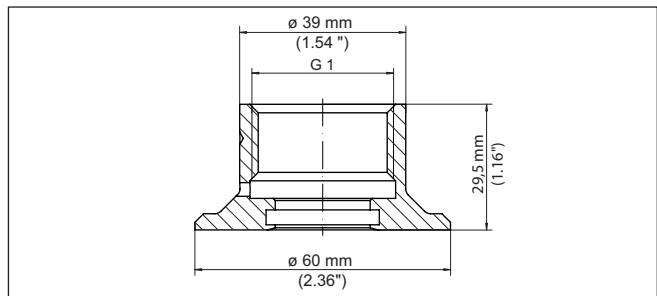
Maße Einschweißstutzen G1 (DIN 3852-A, ISO 228-1) mit Leckage-Bohrung
